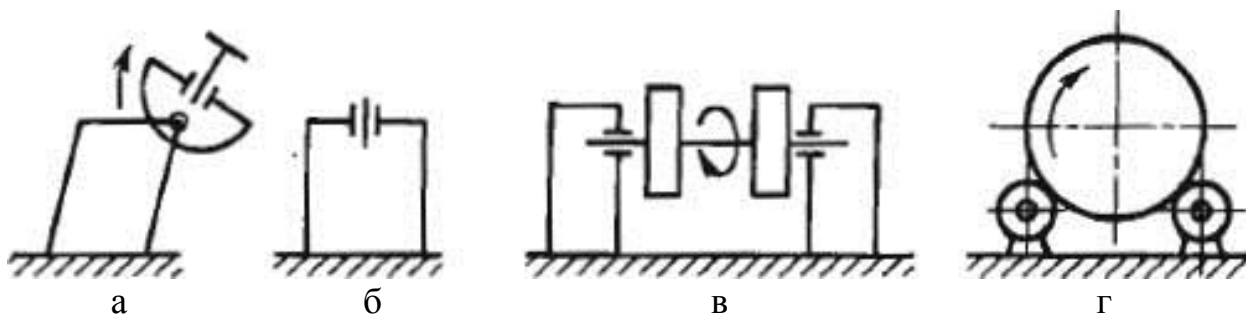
Схемы устройств для позиционирования свариваемых изделий: а – универсальный вращатель, б – вращатель, в – кантователь, г – роликовый вращатель
